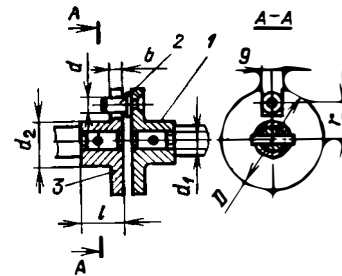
Конструкция однопальцевой поводковой муфты
